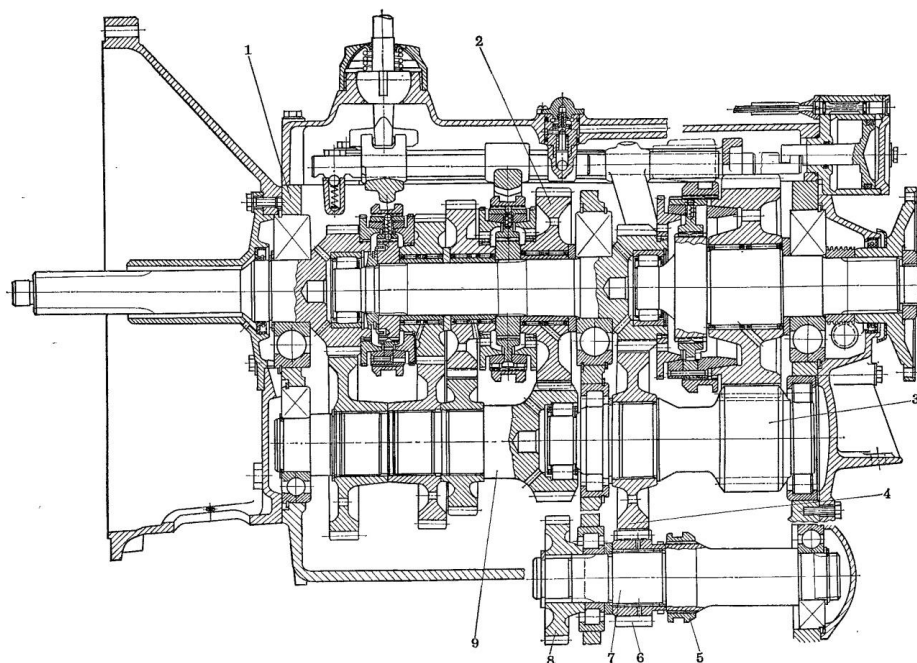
8-ступенчатая коробка передач Volvo R-65
